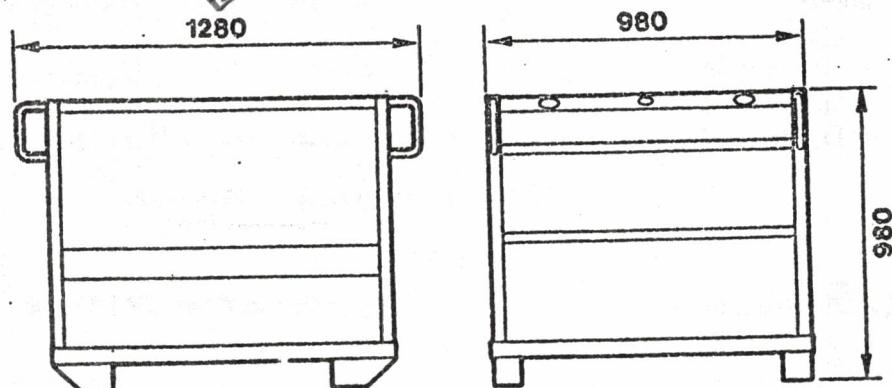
Maßskizze, Drucklufterzeuger (EliMot)
